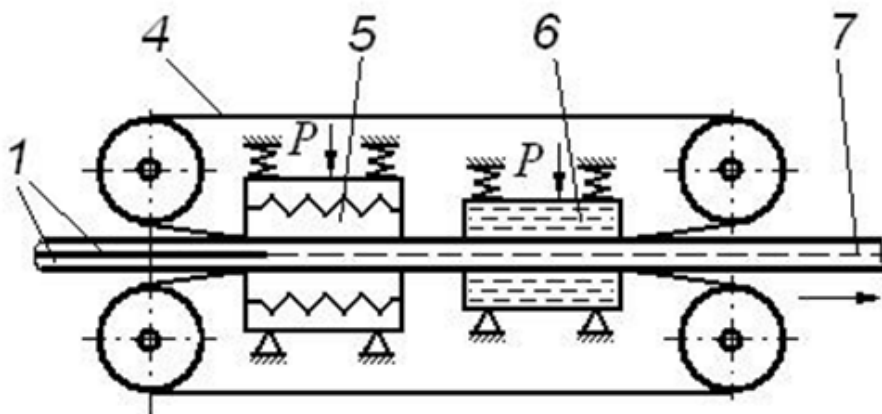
Схема стрічкового зварювання: 1 - зварювальний матеріал; 2 - притискний ролик; 3 – нагрітий ролик; 4 – сталева стрічка; 5 – нагрівальні губи; 6 – охолоджувальні губи; 7 – зварний шов.
